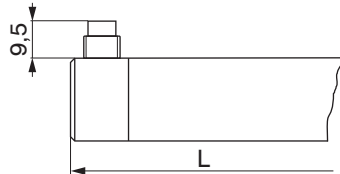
Wegsensor Typ - SR mit radialer Steckverbindung
